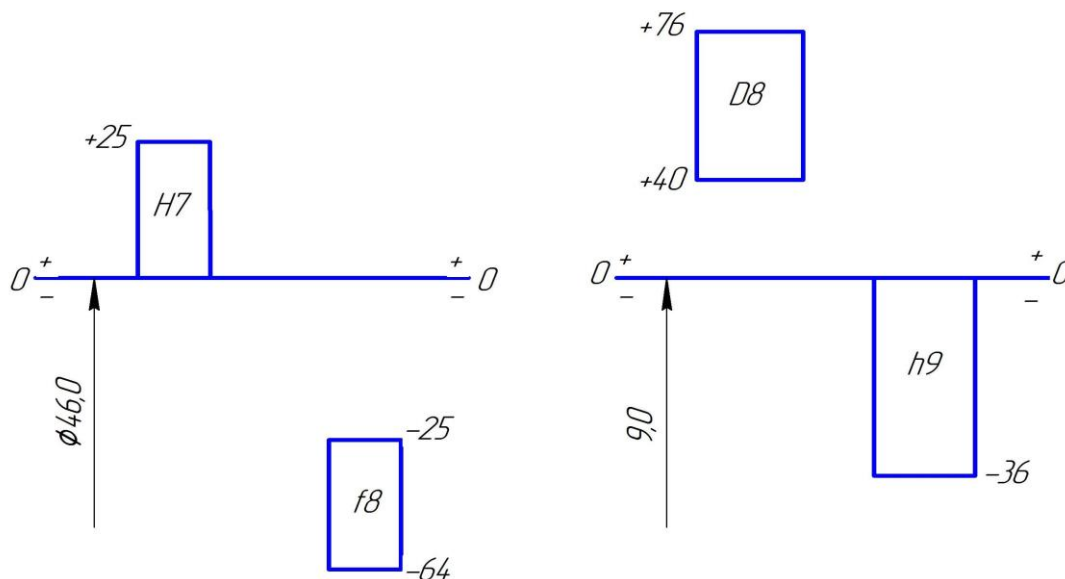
Схемы полей допусков центрирующих элементов прямобочного шлицевого соединения
